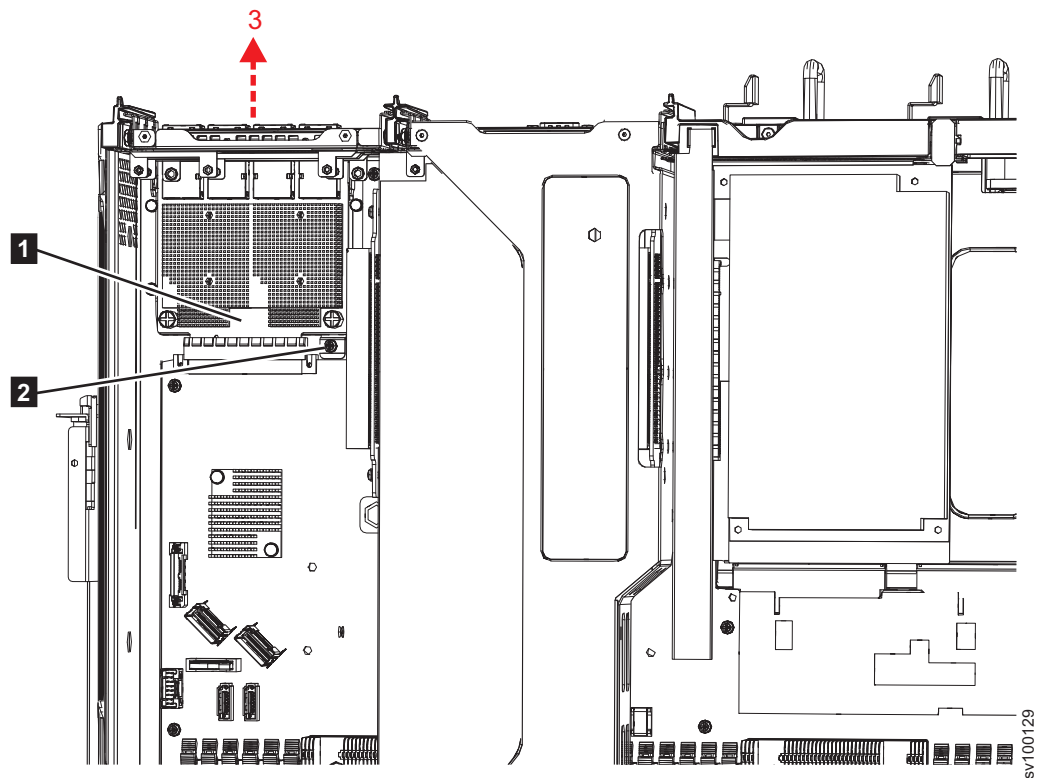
Removendo a Placa de Borda Ethernet do 2145-SV1
